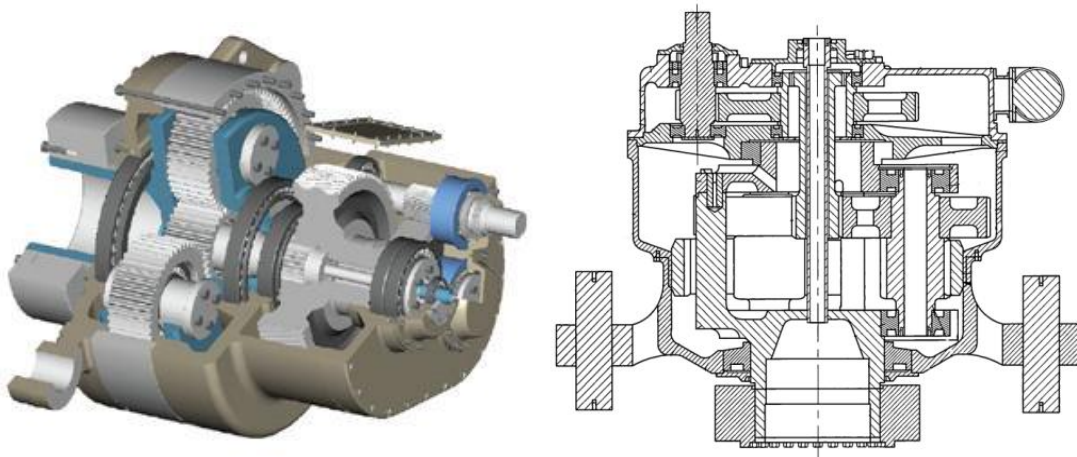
spaccato assonometrico e sezione di un gearbox
